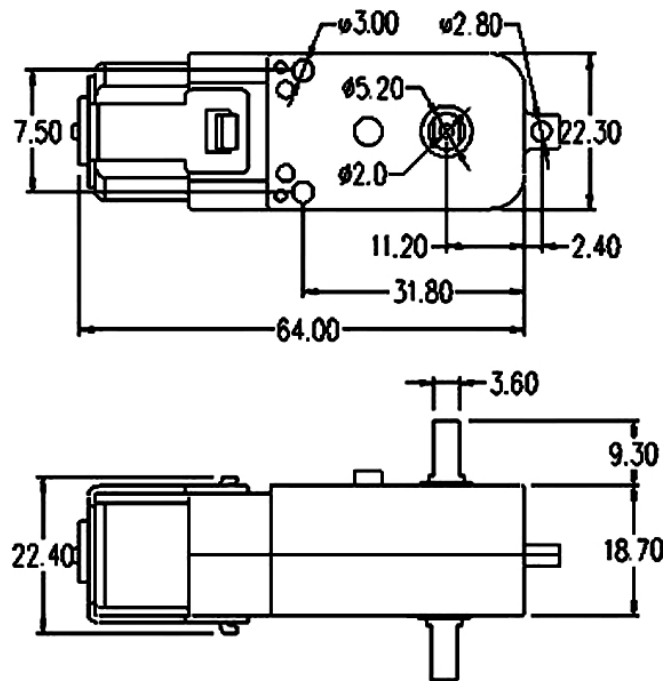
Загальний вигляд двигуна з редуктором 1:48
